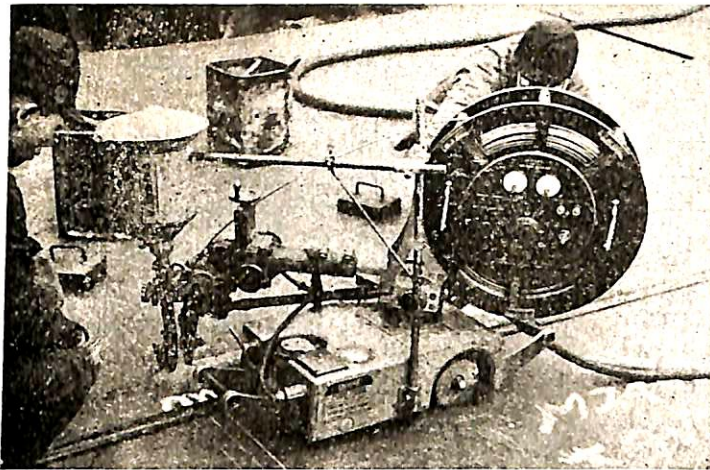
溶接作業中の Union Melt Welding Machine (Linde DS-37)
